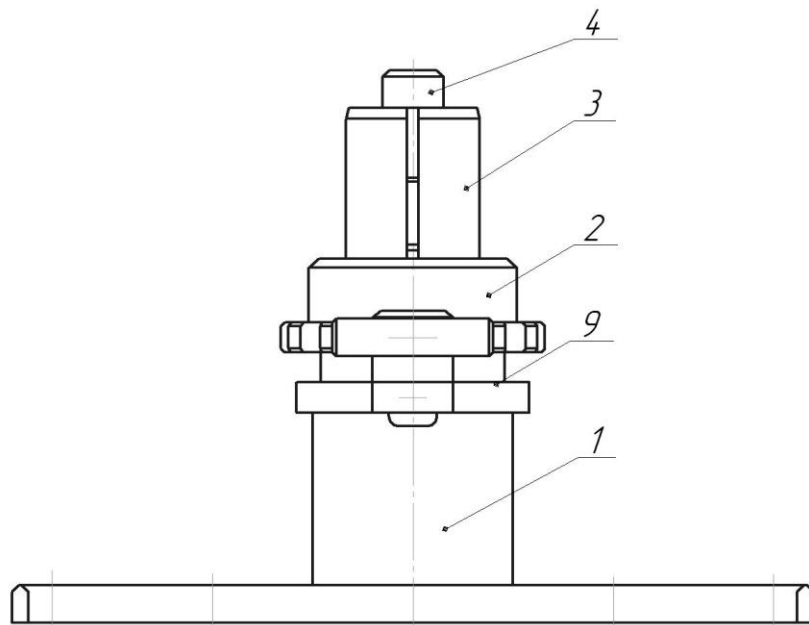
Пристрій для фіксування веденого диска при висвердлюванні заклепок (вид з боку керування)
